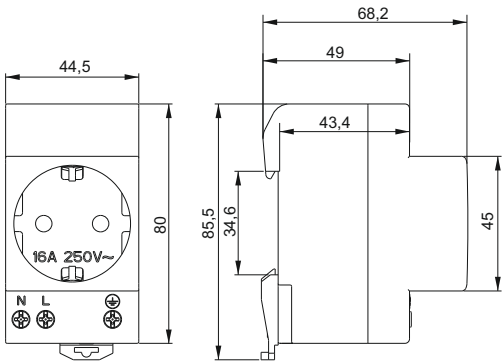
Габаритные и установочные размеры / Figure 2 – Overall and mounting dimensions
